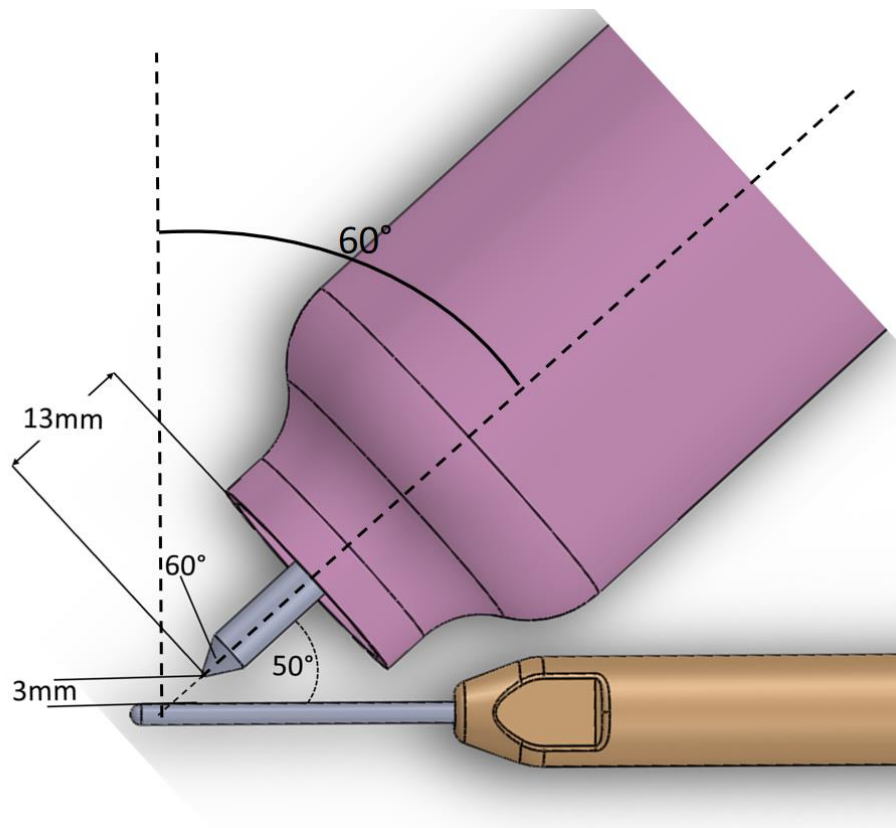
Distâncias e ângulos utilizados na tocha de soldagem.
